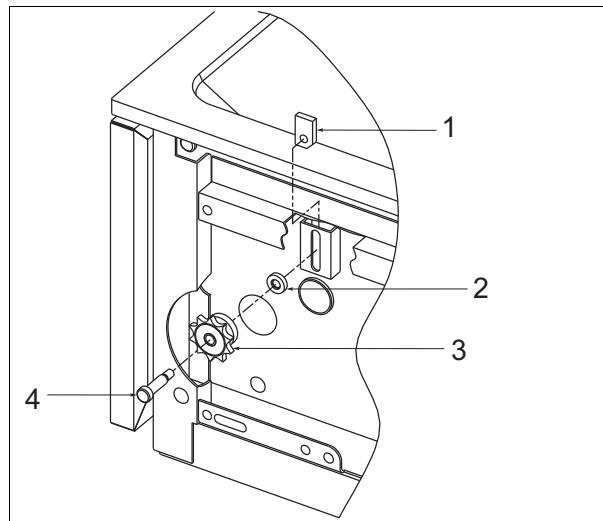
Assemblage de la roue dentée de la poulie de renvoi
